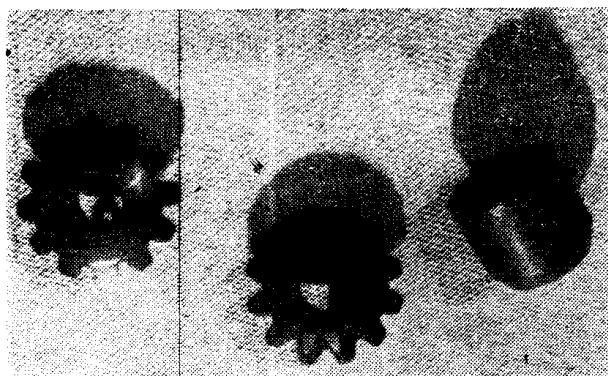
行星齿轮予制坯及未经任何加工的东方红-20粉锻行星齿轮
